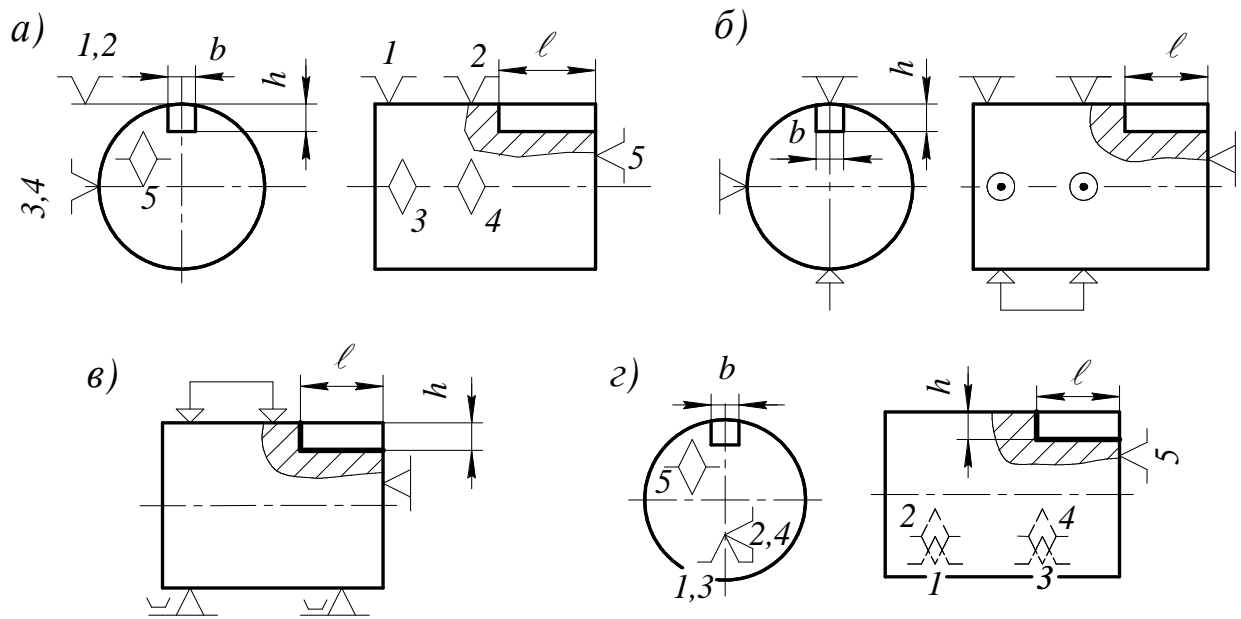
Теоретические схемы базирования (*а, з*) и схемы установки заготовки (*б, в*) при обработке шпоночного паза
